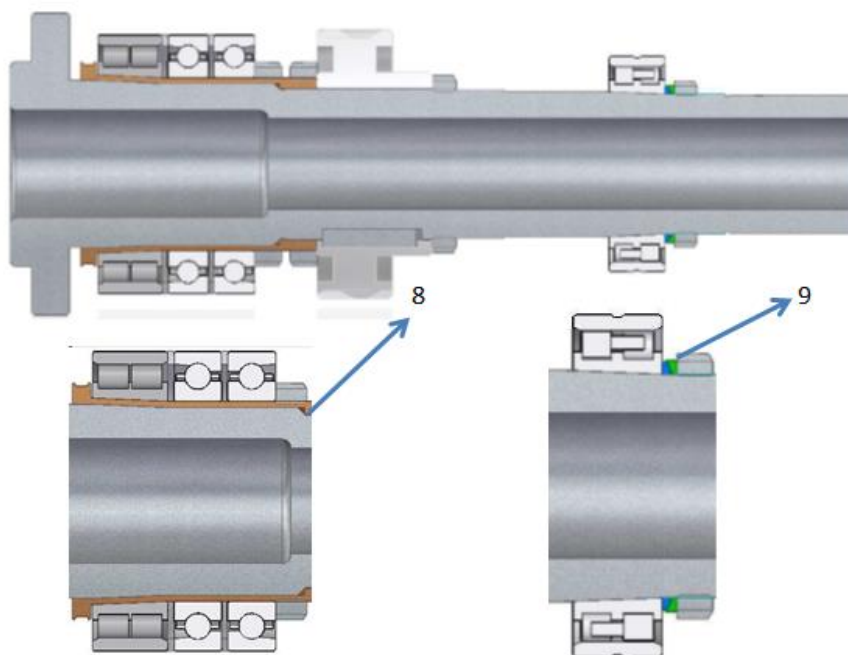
Ansamblu arbore principa cu sistem de compensare
